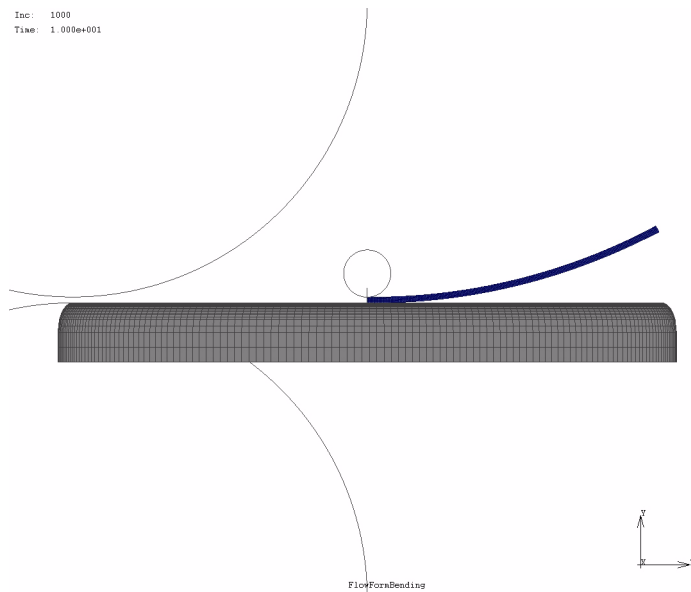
Minirolle/Querrolle - Seitenansicht
